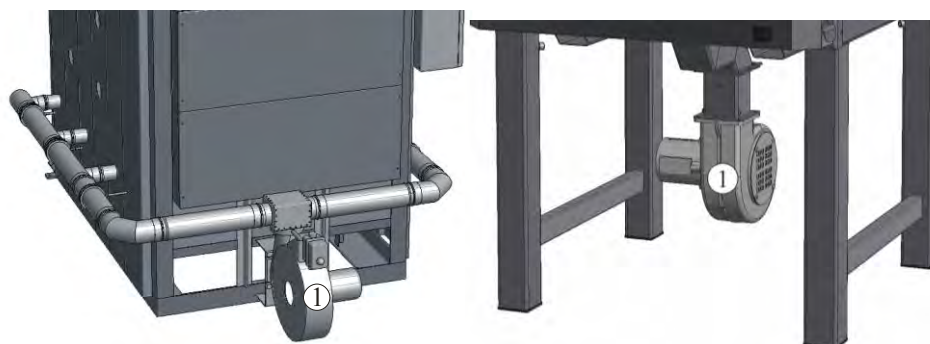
ventilation d'air frais et/ou d'air de refroidissement (figure analogue)
